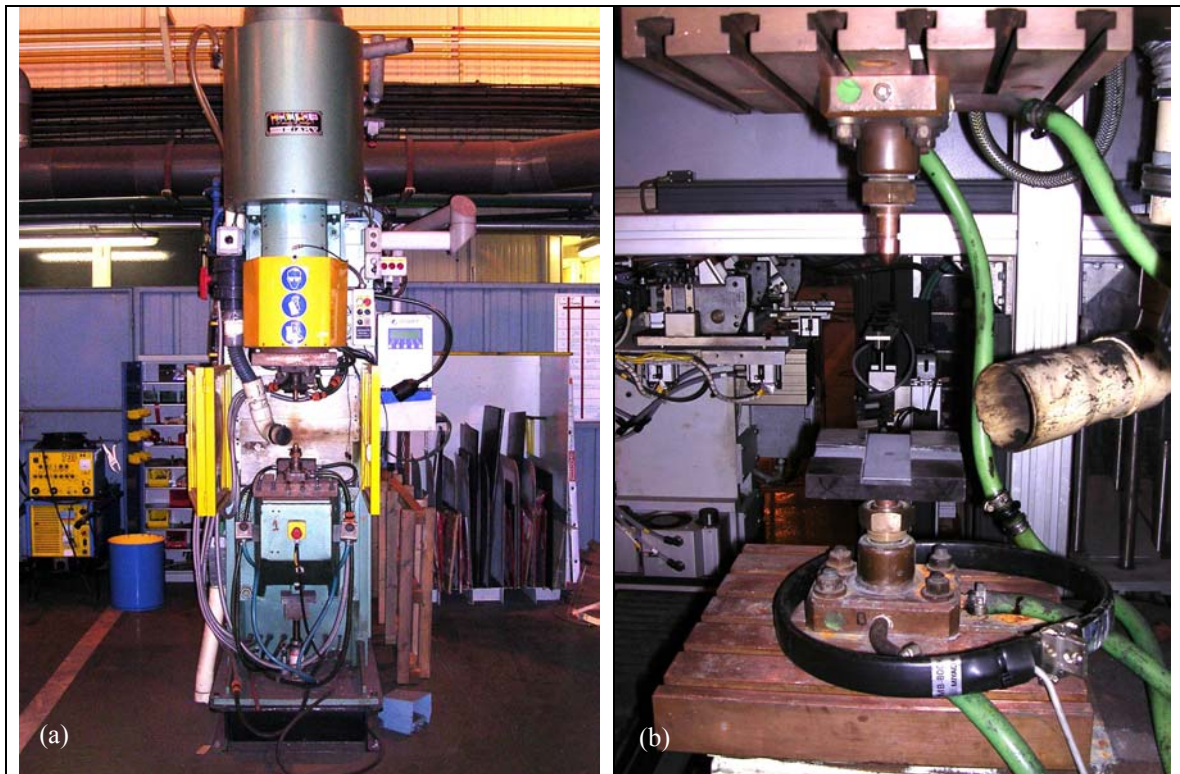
Appareillage d'essai de soudage par points : a) Machine de soudage «SCI AKY», b) Eprouvette de traction en croix entre deux électrodes
